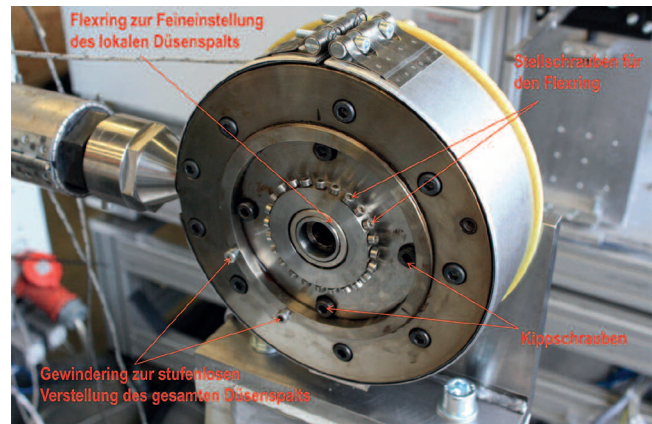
Kopf zur Herstellung von Bewässerungsschläuchen mit Kippdüse mit einer Flexringhülse, mit einer stufenlosen Düsenspaltverstellung und mit einer speziellen Verteilerkanallösung, um eine sehr kurze Baulänge zu ermöglichen
